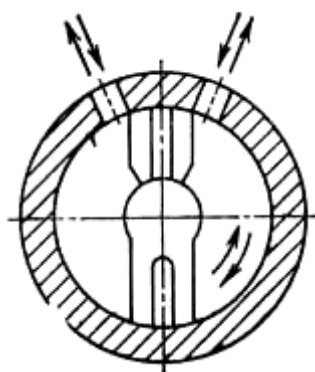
Схема пластинчатого поворотного двигателя с одной пластиной
